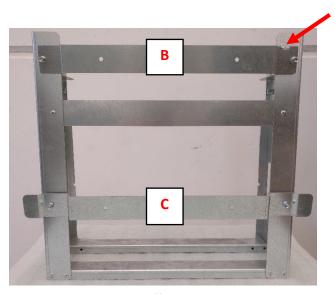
Installazione staffe sul box batterie: il verso di installazione
